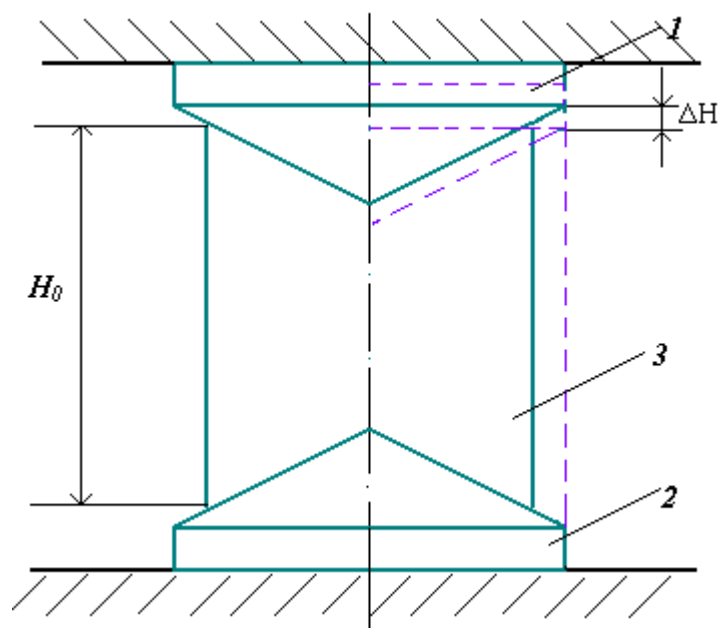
Осадка заготовки сторцевыми углублениями на конусных бойках: 1,2 – верхний и нижний бойки; 3 – заготовка.
